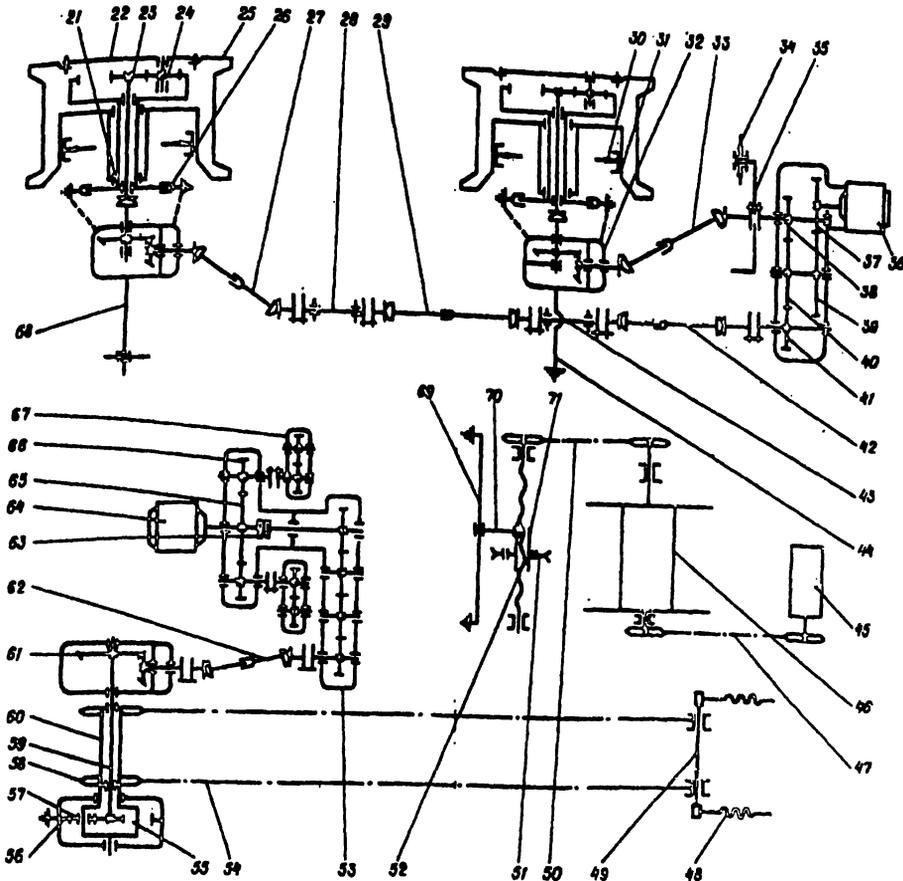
Кинематическая схема шахтного самоходного вагона 5BC-15M
